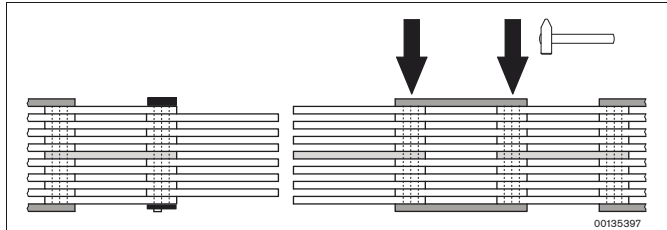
Kürzen: Schweißnaht sprengen
